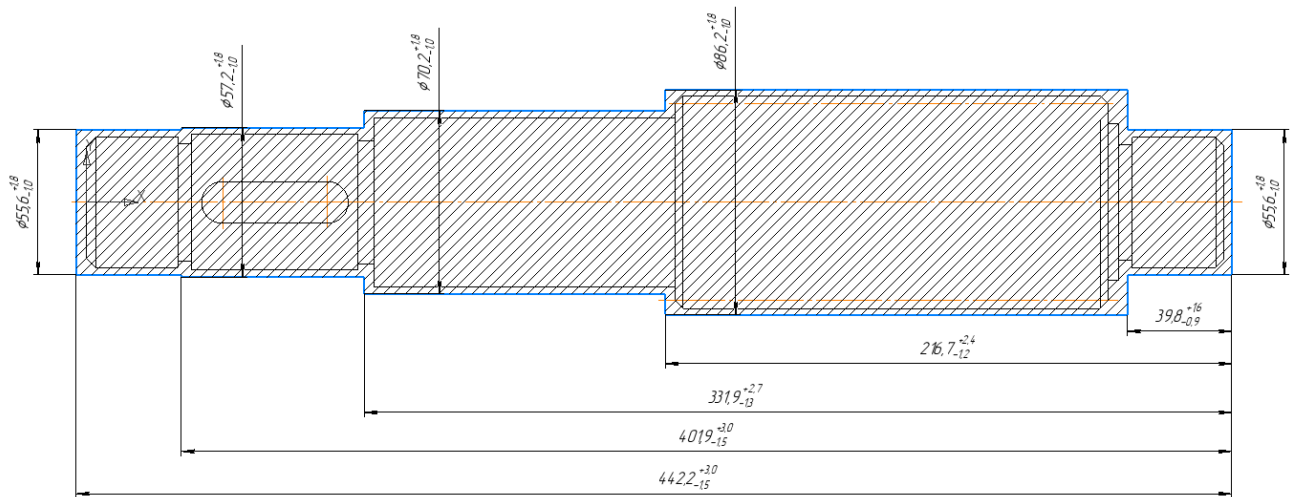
Ескіз заготовки виготовленої на ГKM
